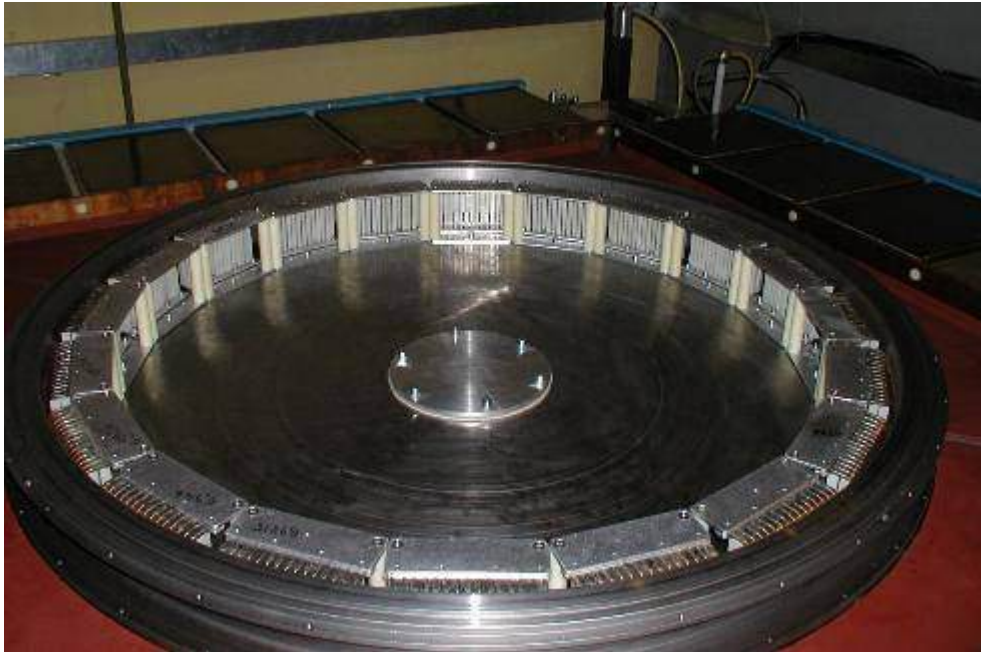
Вид ступени со снятым верхним фланцем и установленными резисторами нагрузки
